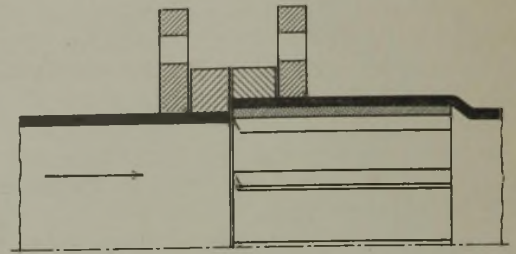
Zylindrisch erweiterte Eintrittseite mit eingepreßtem Verschleißring.
